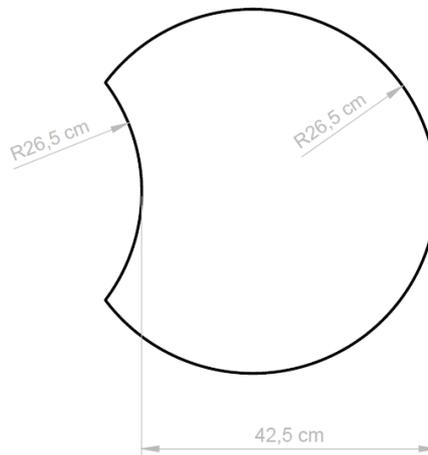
Dimensiones asiento silla. Fuente: Autocad
